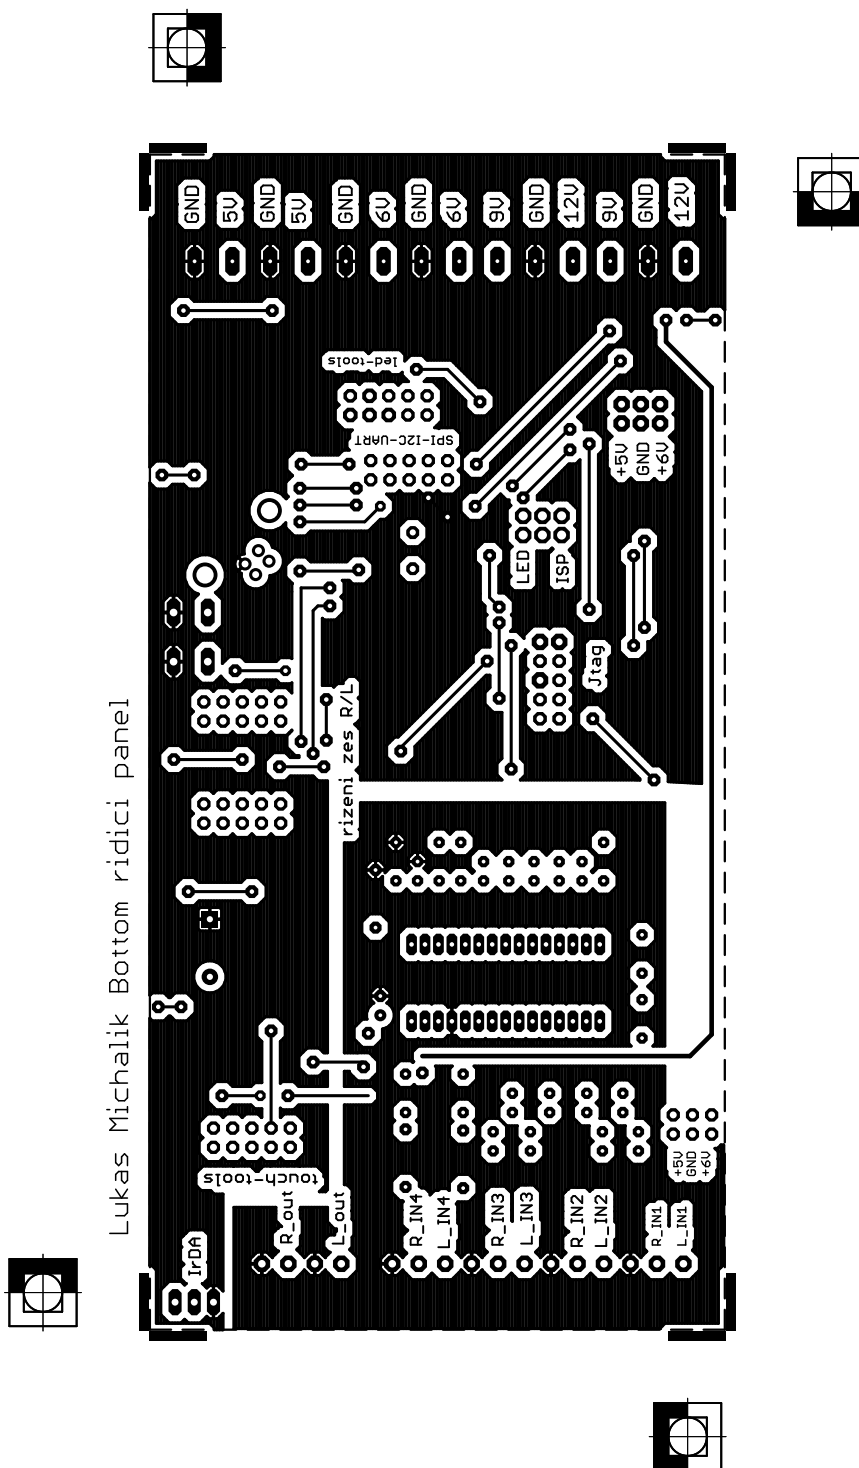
Ovládací panel - bottom (scale 0,6)
